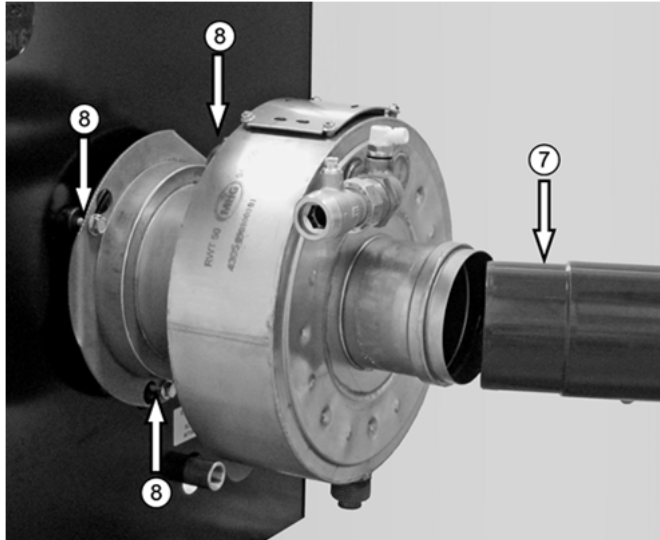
Demontage Abgasrohr Kesselanschluss und RWT
